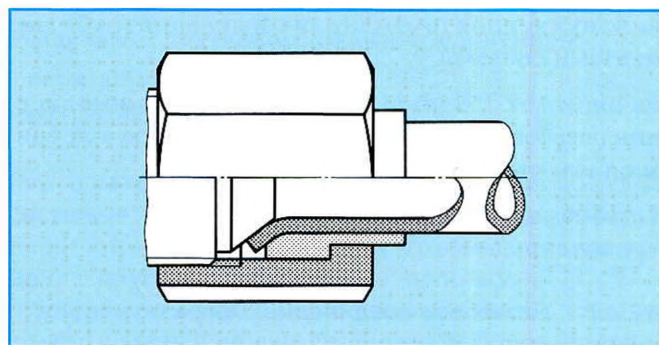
Резьбовое соединение с уплотняющей отбортовкой. Уплотнение: металл по металлу. Фиксация осуществляется при помощи отбортовки под углом 37°, прижимаемой к проточке на штуцере.
